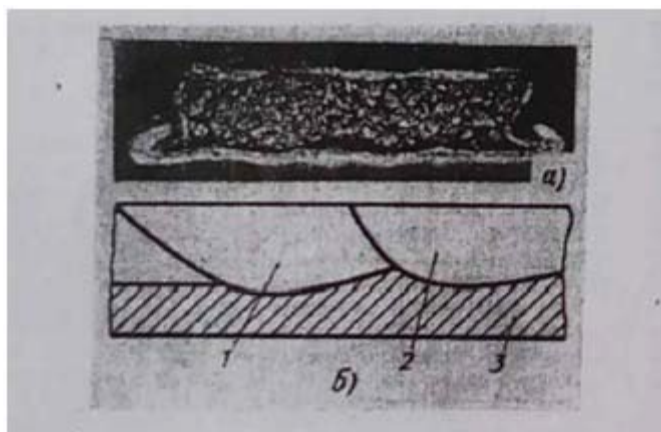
Схема наплавки. 1 – предыдущий валик, 2 – последующий валик, 3 – основной металл.
